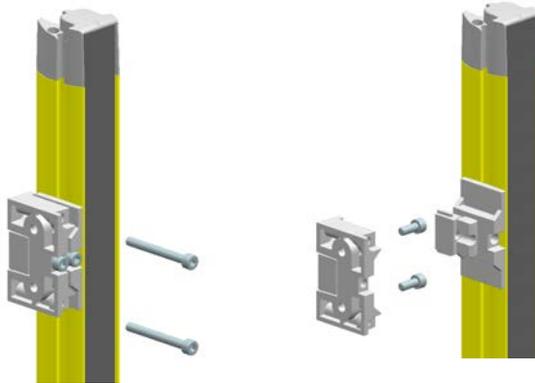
Montage über schwenkbare Halter BT-2SB05 und M5-Schrauben
